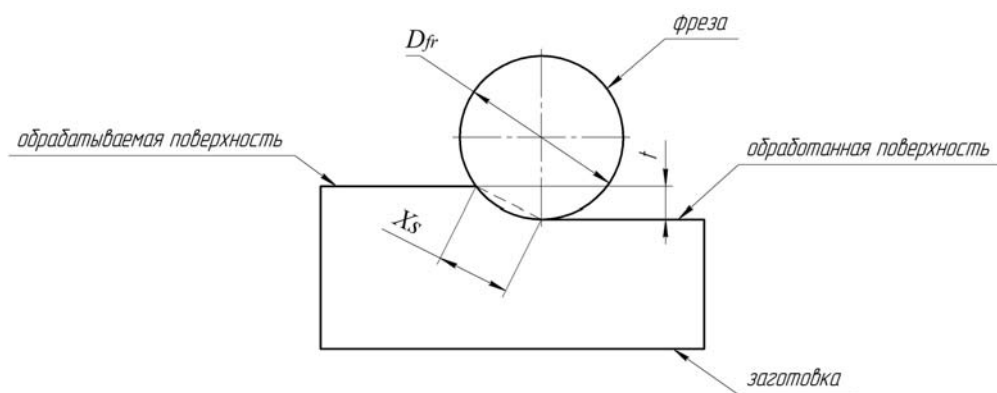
Взаимное расположение фрезы и обрабатываемой заготовки в процессе фрезерования, X_s – длина хорды
